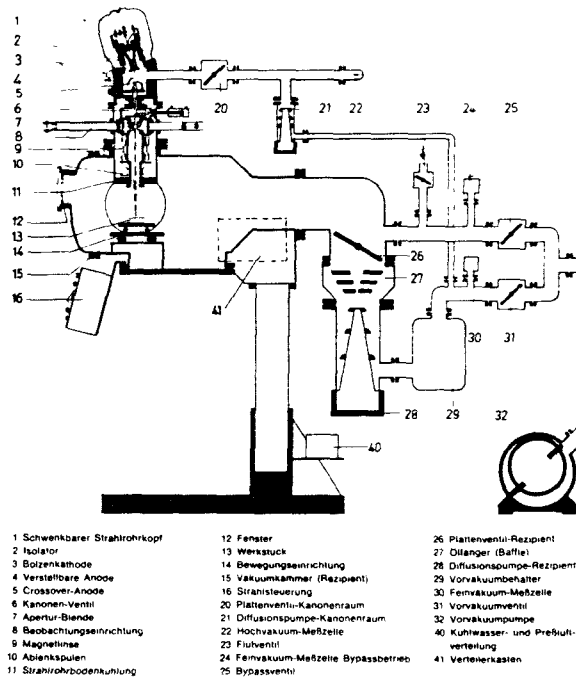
Schema der Elektronenstrahl-Schweißmaschine-ESW5 der Fa. Balzers
